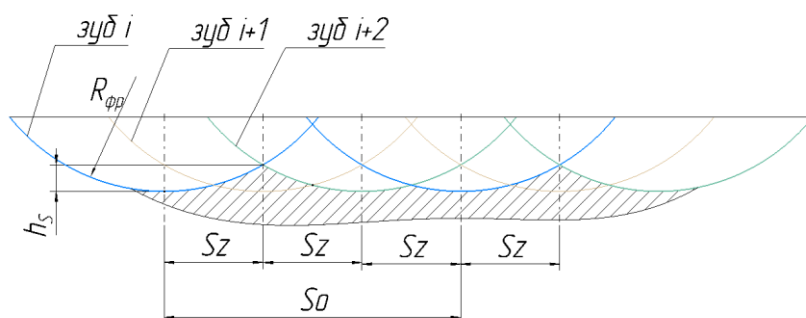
Схема образования неровностей фрезой со стружкоделительными канавками
